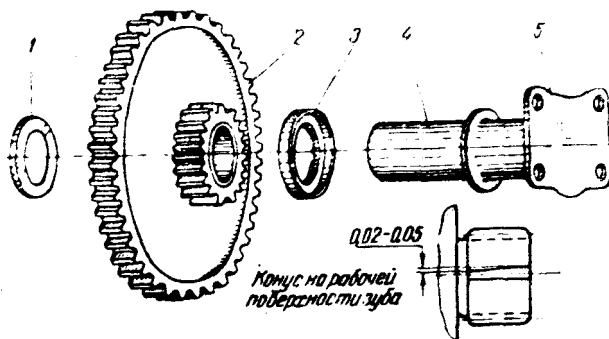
Двойная шестерня привода крыльчатки нагнетателя с осью: 1—шайба передняя; 2—двойная шестерня; 3—шайба задняя; 4—ось шестерни; 5—фланец оси
